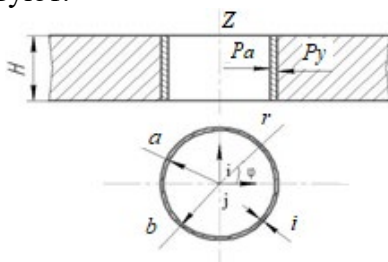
Схема цилиндра, охватывающего деформированный поверхностный слой отверстия под давлением на него внутренних и внешних сил
